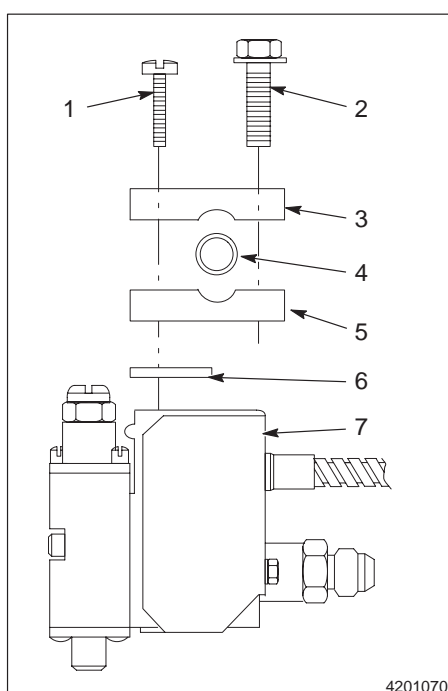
Installation d'un pistolet H-200 standard sur une barre de montage
